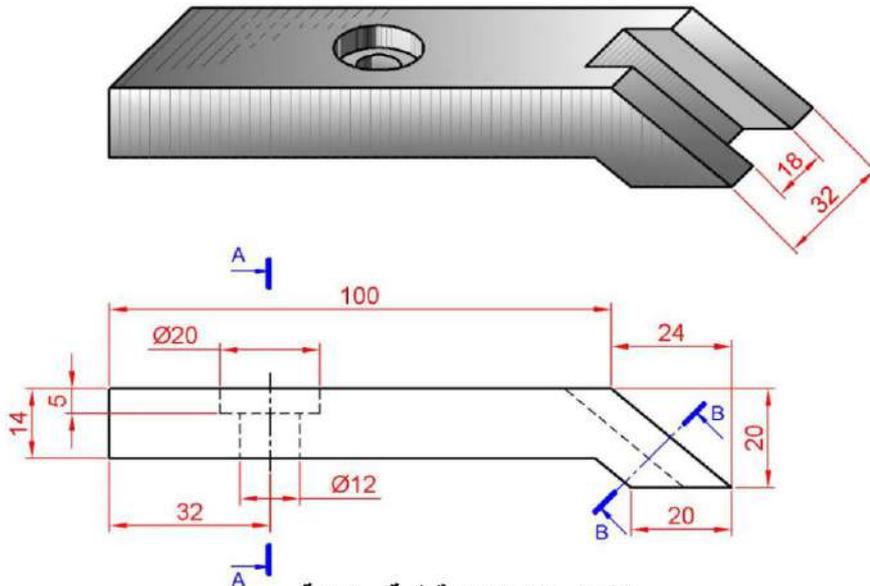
المسقطان الأمامي والأفقي لمشغولة
